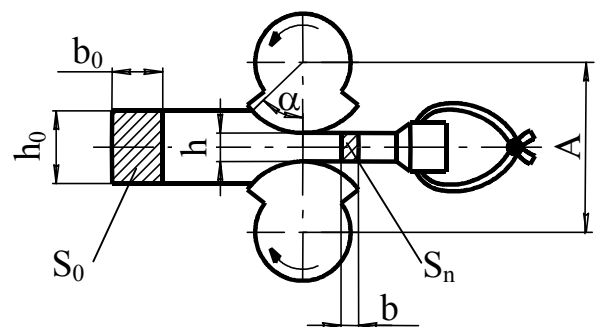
Схема вальцювання: h_0 , b_0 і h , b – висота і ширина заготовки до і після вальцювання
